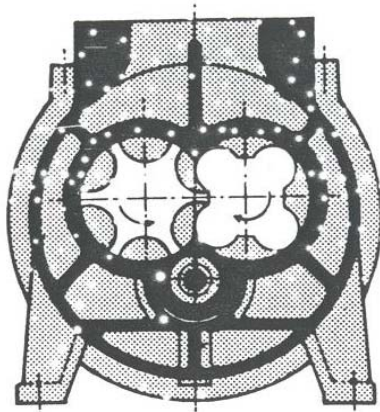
Rotación de los rotores birrotor de tornillo (York) de un compresor birrotor
